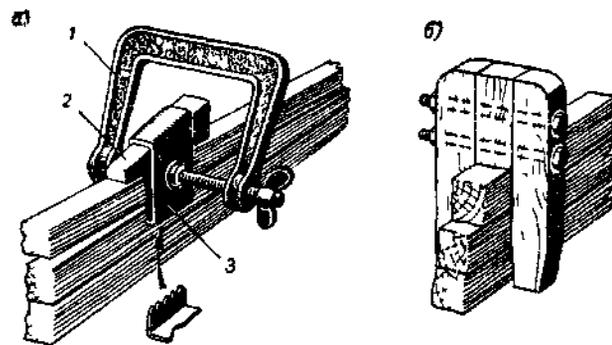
Приспособления для сборки реечной обшивки: а — клиновой прижим к струбцине; б — цвинка. 1 — струбцина, 2 — клин, 3 — обойма захват
